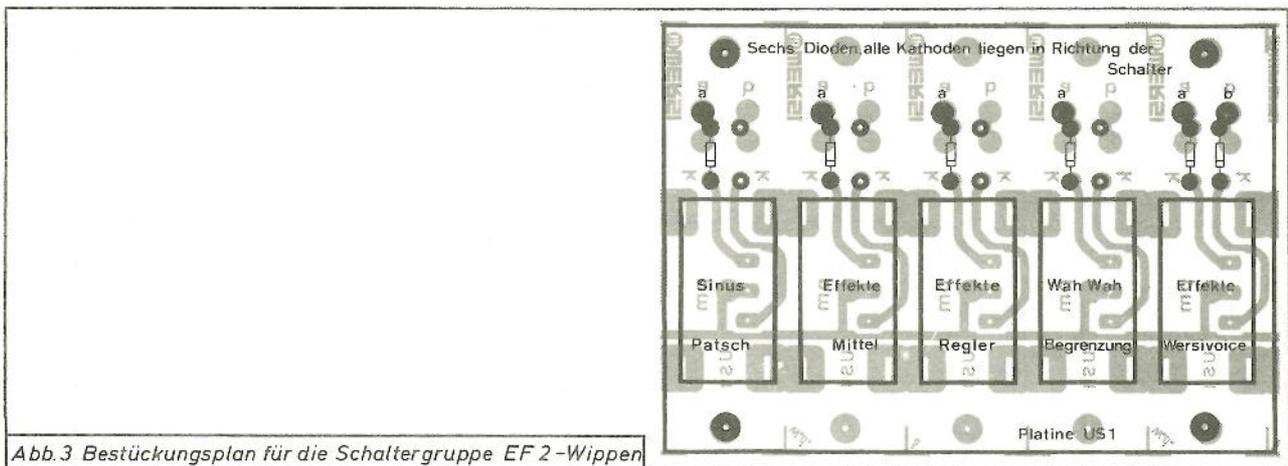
Bestückungsplan für die Schaltergruppe EF 2 - Wippen
